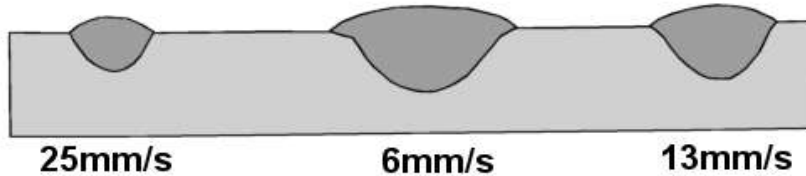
Representação da seção transversal de cordões de solda depositados por SAW em chapas de aço carbono mostrando a influência da corrente, tensão e velocidade de soldagem no formato do cordão (adaptado do AWS Welding Handbook Vol. 1)..
